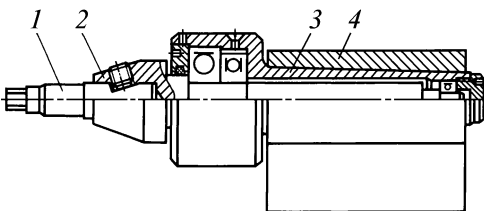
Приспособление для обработки внутренних многогранников:
